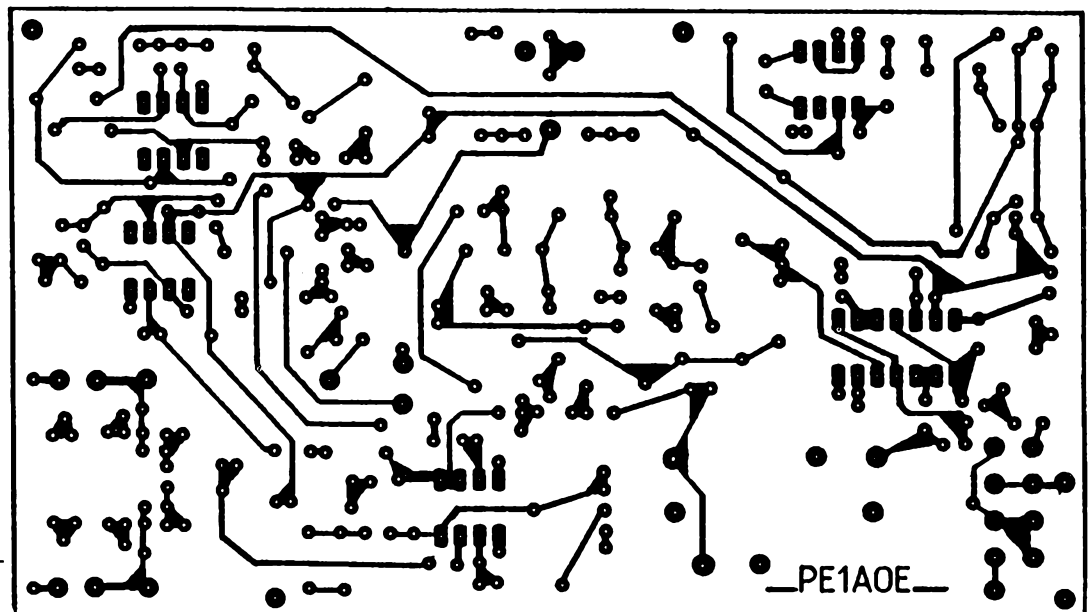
Printlay-out, de componentenzijde is geheel van koper.
